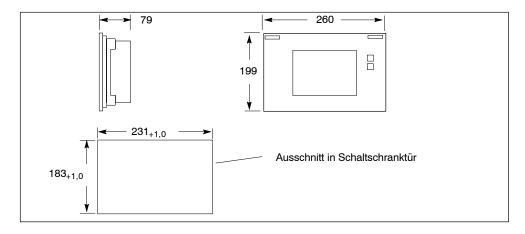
Maßbilder für das C7-635 Touch (Maße in Millimeter)
